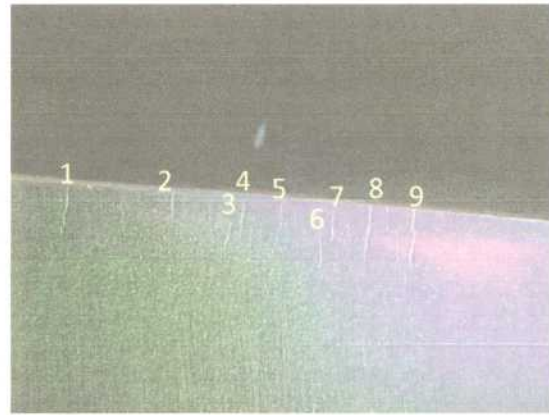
Fisuras en el álabe nº 53.
